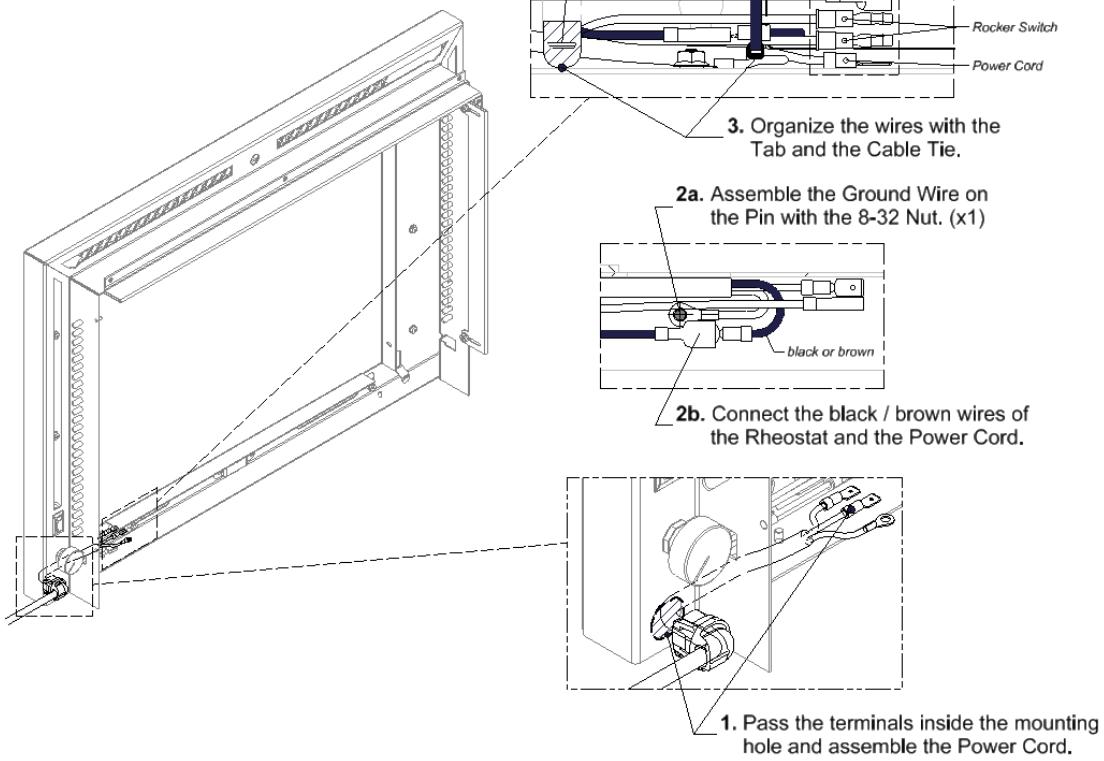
Installation du cordon d'alimentation (sortie de la façade)
